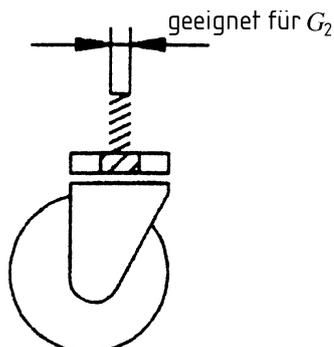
Befestigungsbolzen-Durchmesser für Rückenlochbefestigung
